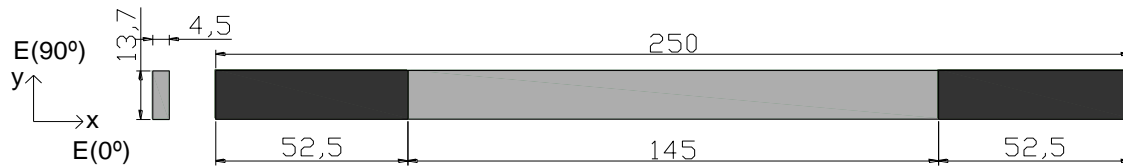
Probeta del ensayo con las direcciones longitudinal y transversal.
